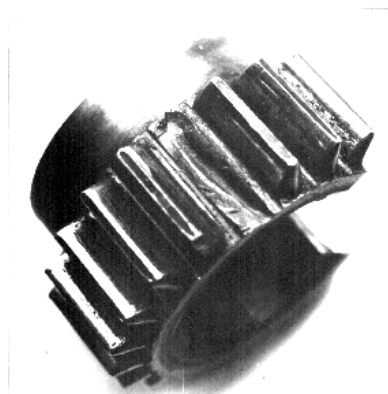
Разрушение двух зубьев шестерни из стали 45 коробки 1А61, передач токарного станка
